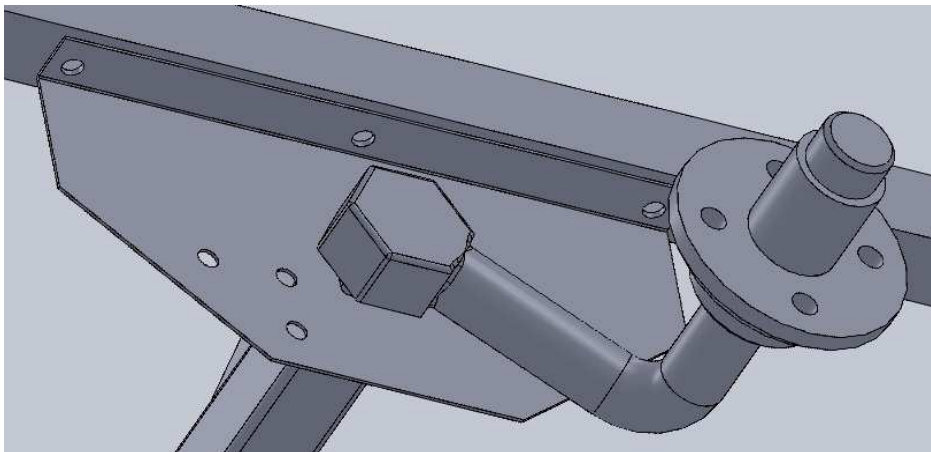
Konstrukční návrh přívěsu – varianta 2. Celkový pohled.
